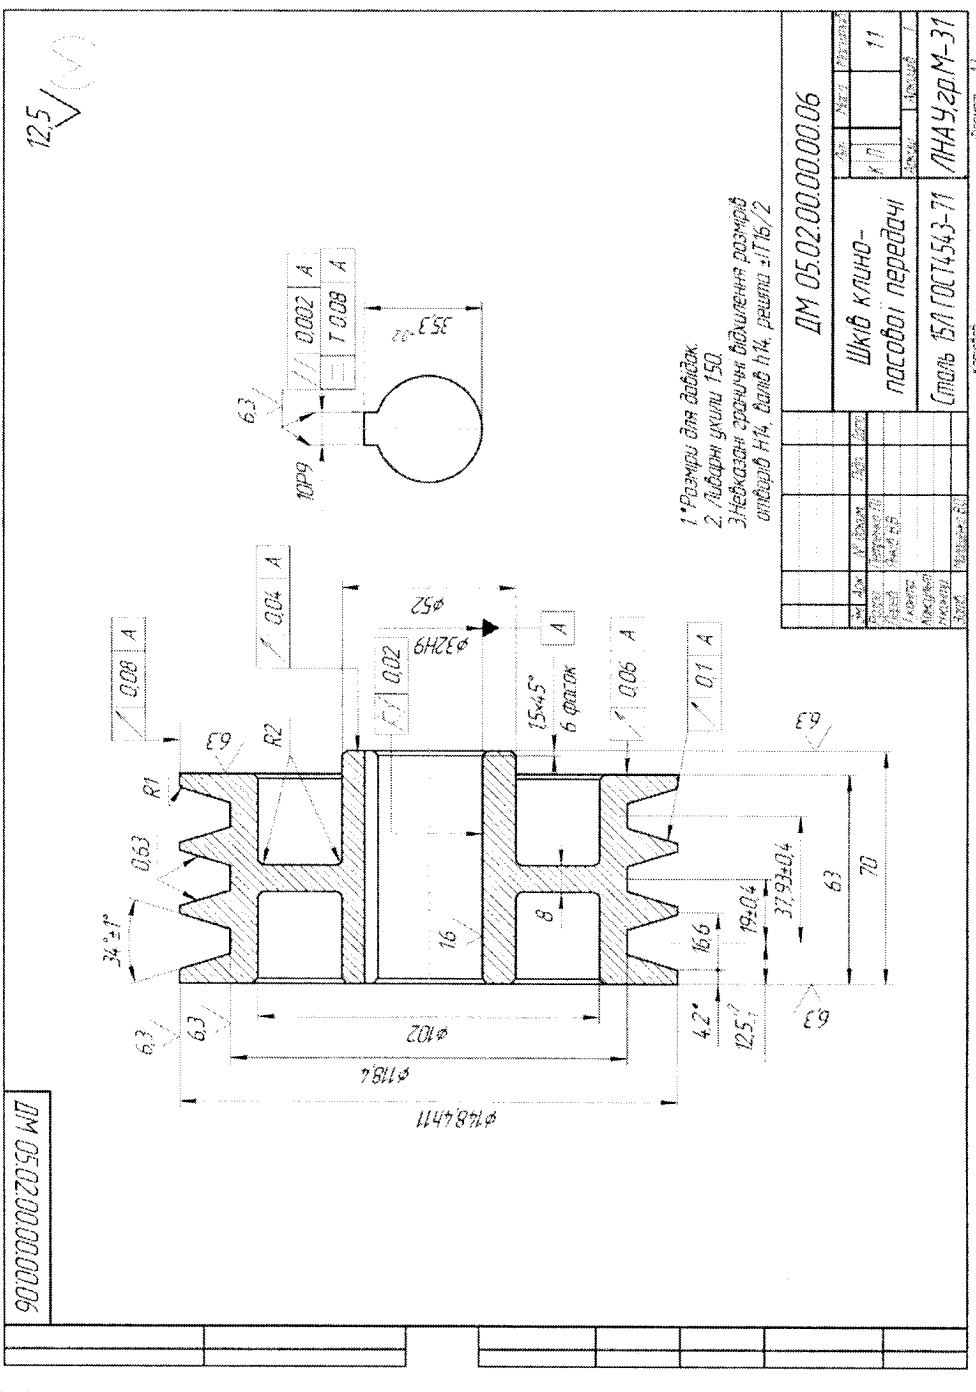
Приклад робочого креслення шкiва клинопасосаби передачи
